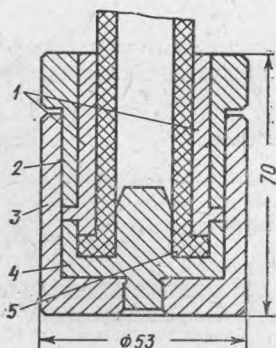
Пресс-форма для формирования буртов полиэтиленового шланга:
